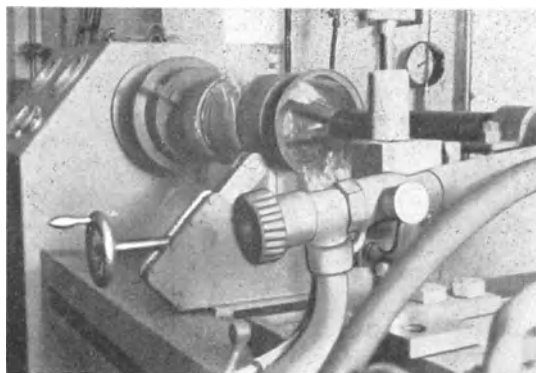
Innenhärtung auf einer Waagrecht-Härtemaschine.
